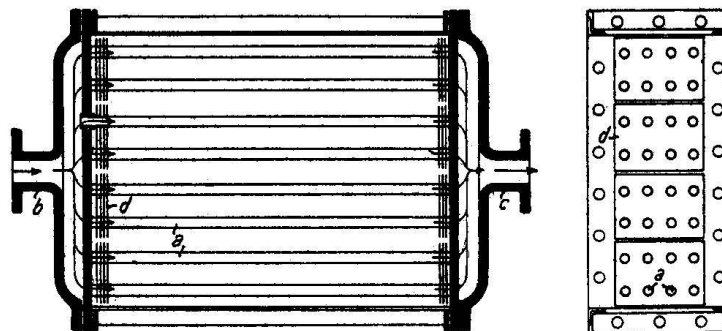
, Einspritzkühlvorrichtung von Moll & Co.
